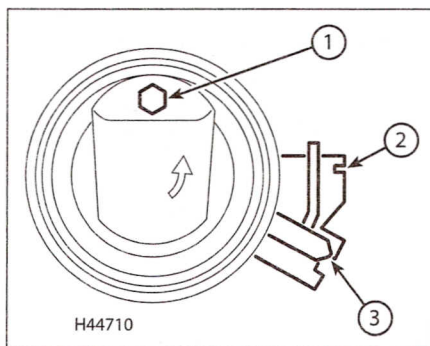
Натяжитель ремня газораспределительного механизма (поздние двигатели 1.4 л)
